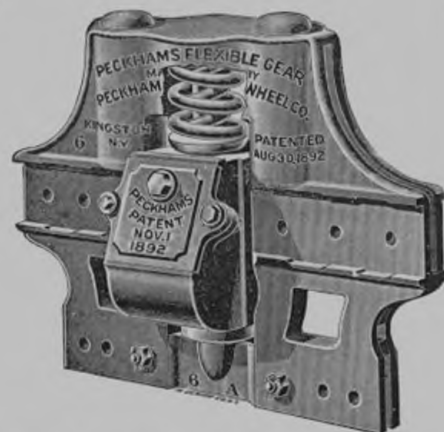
PLAQUE DE GARDE ET BOÎTE DU CHASSIS PECKHAM
